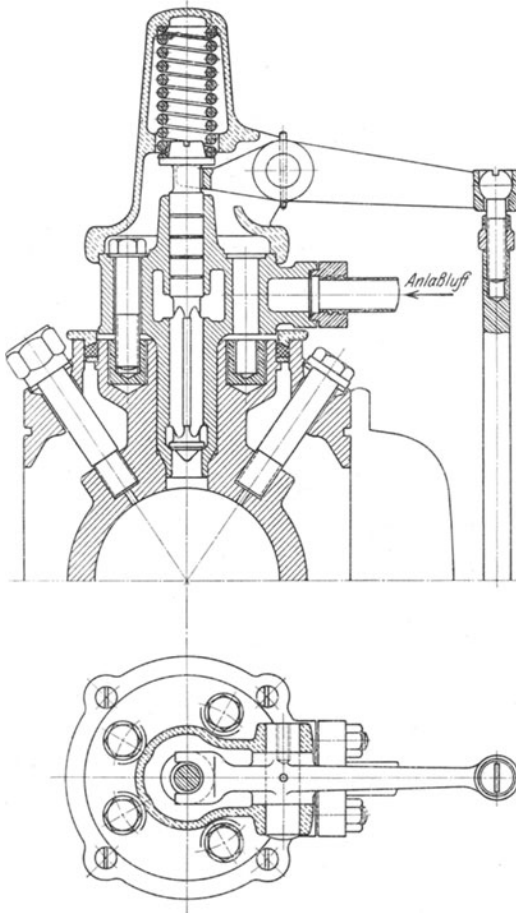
39. Anlaßventil mit nach außen öffnender Spindel.
